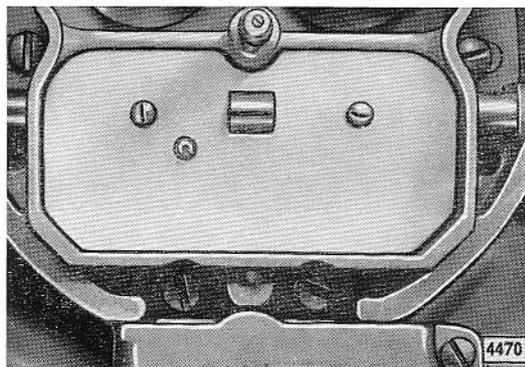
Luftklappe eingebaut – Bezeichnung „C“ von Oberseite des Vergasers sichtbar
